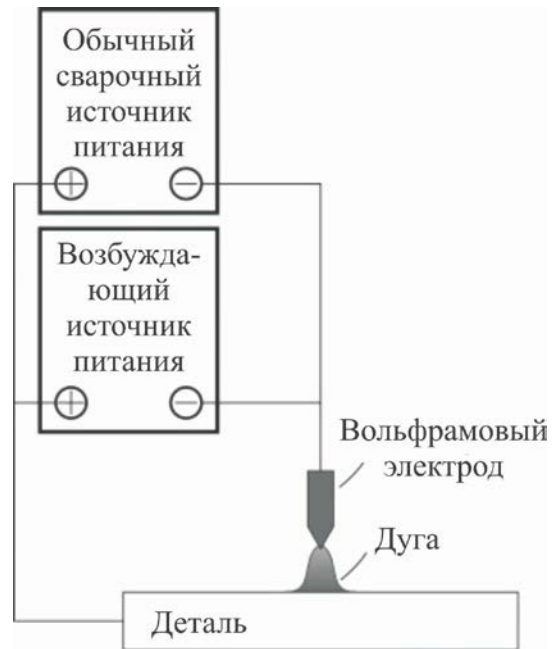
Схема ультразвукового возбуждения сварочной дуги
